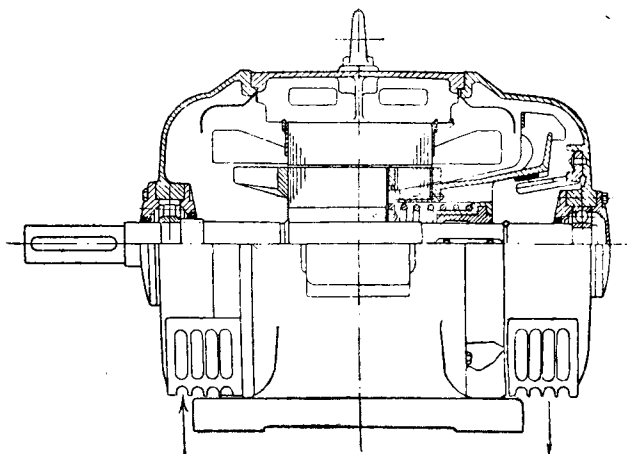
Двигатель фирмы Саксенверк со встроенным тормозом, управляемым от поля якоря (внешний вид и разрез)
